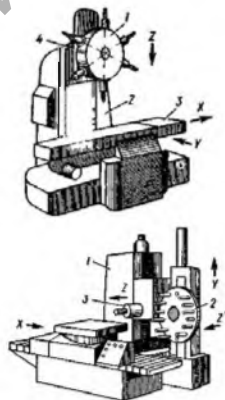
Компоновка многооперационных станков на базе вертикально-фрезерного станка с револьверной головкой и горизонтально-расточного станка
